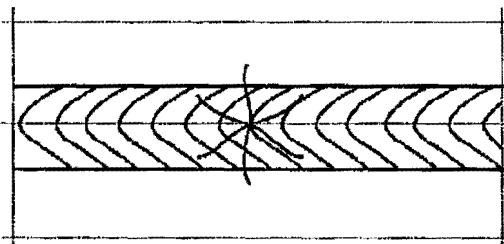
27. Радиальная трещина сварного соединения
